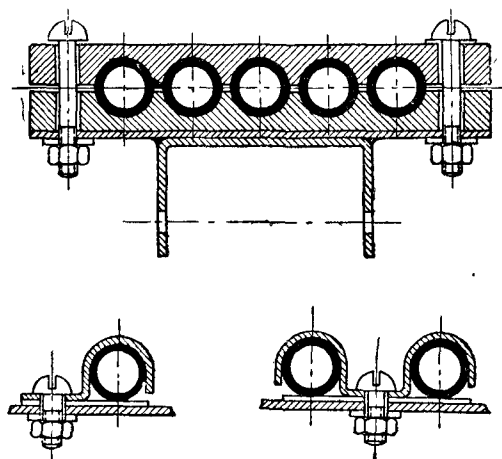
Соединение трубопроводов в месте прохода через противопожарную перегородку.
